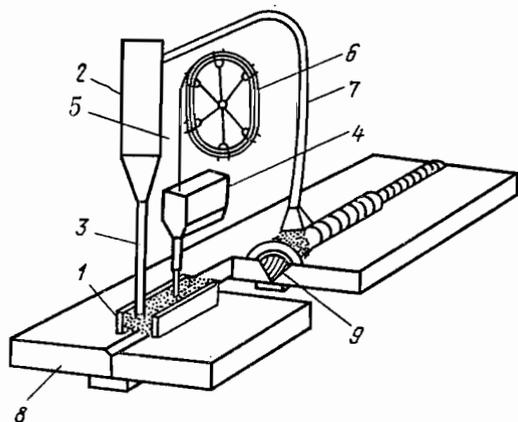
Схема автоматической сварки под флюсом:
